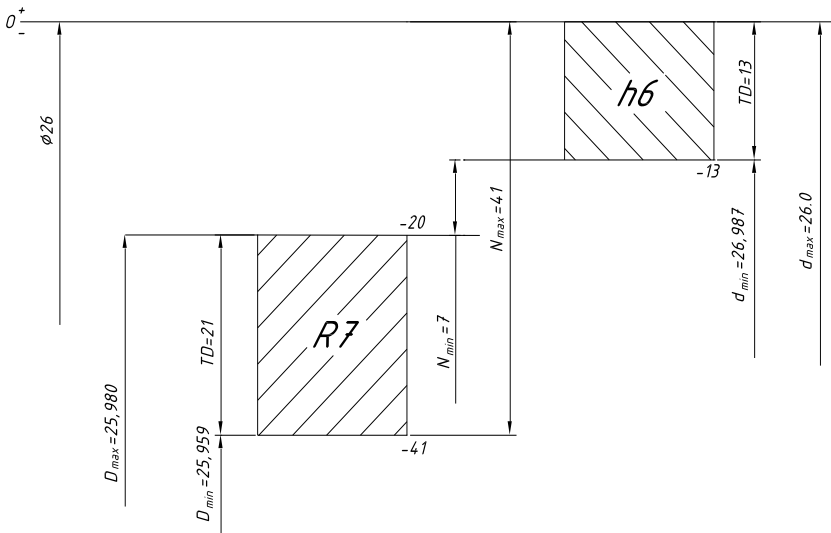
Схема розташування полів допусків з'єднання $\varnothing 26 \frac{R7}{h6}$
